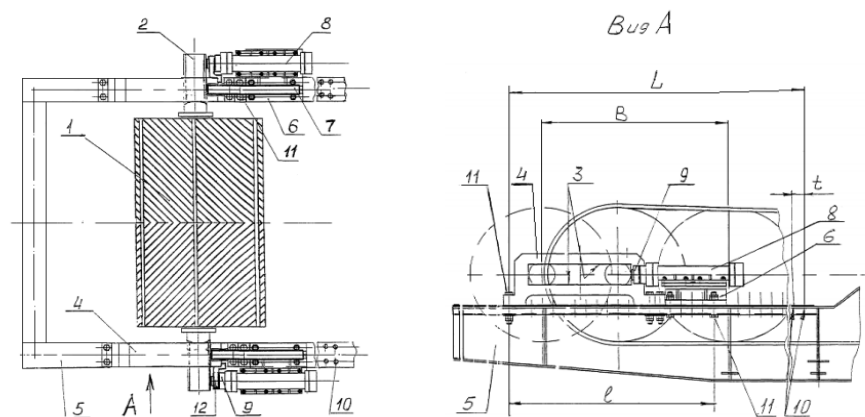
Схема удосконалення конструкції натяжного пристрою для ящикового живильника
